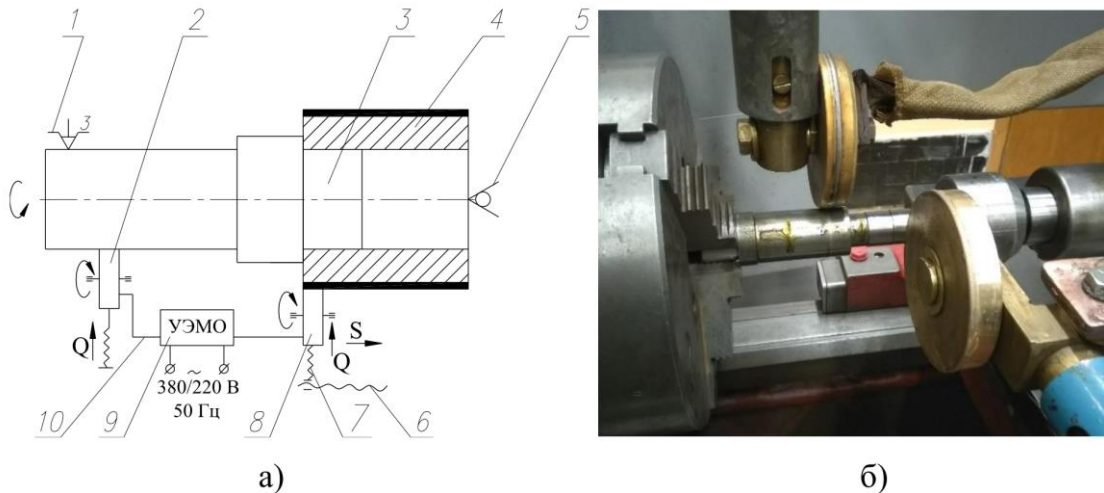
Схема ЕМПЗ: а) принципова схема; б) загальний вигляд. 1 – трикулачковий патрон, що самоцентрується; 2 – струмопідвідний ролик; 3 – оправлення; 4 – зразок; 5 – обертовий центр; 6 – ходовий гвинт верстата; 7 – телескопічна державка; 8 – інструментальний ролик; 9 – установка електромеханічного оброблення; 10 – струмопідвідні шини.
